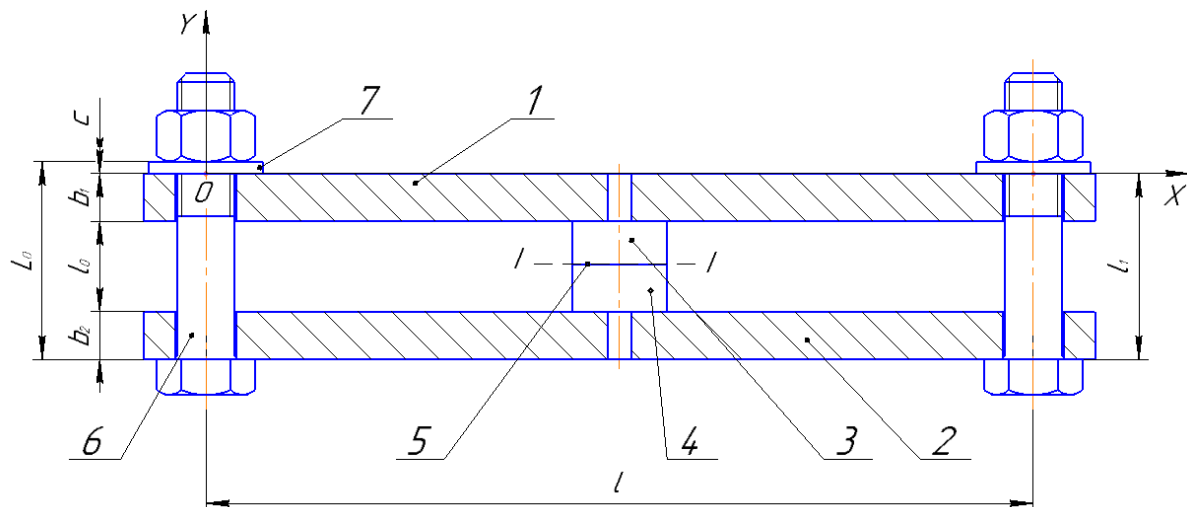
Розрахункова схема пристрою для зварювання зразків:
